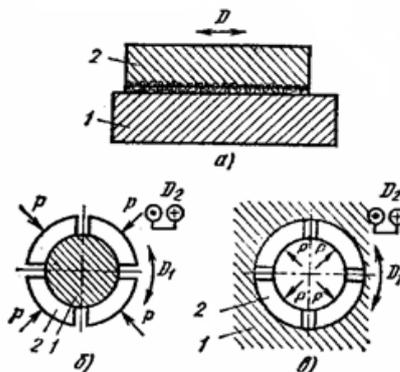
Схемы притирки: а – плоской, б – наружной цилиндрической, в – внутренней цилиндрической поверхностей
